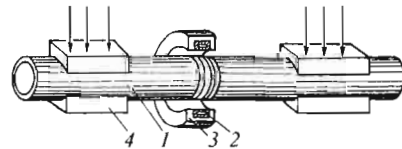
Схема стыковой высокочастотной сварки труб:
